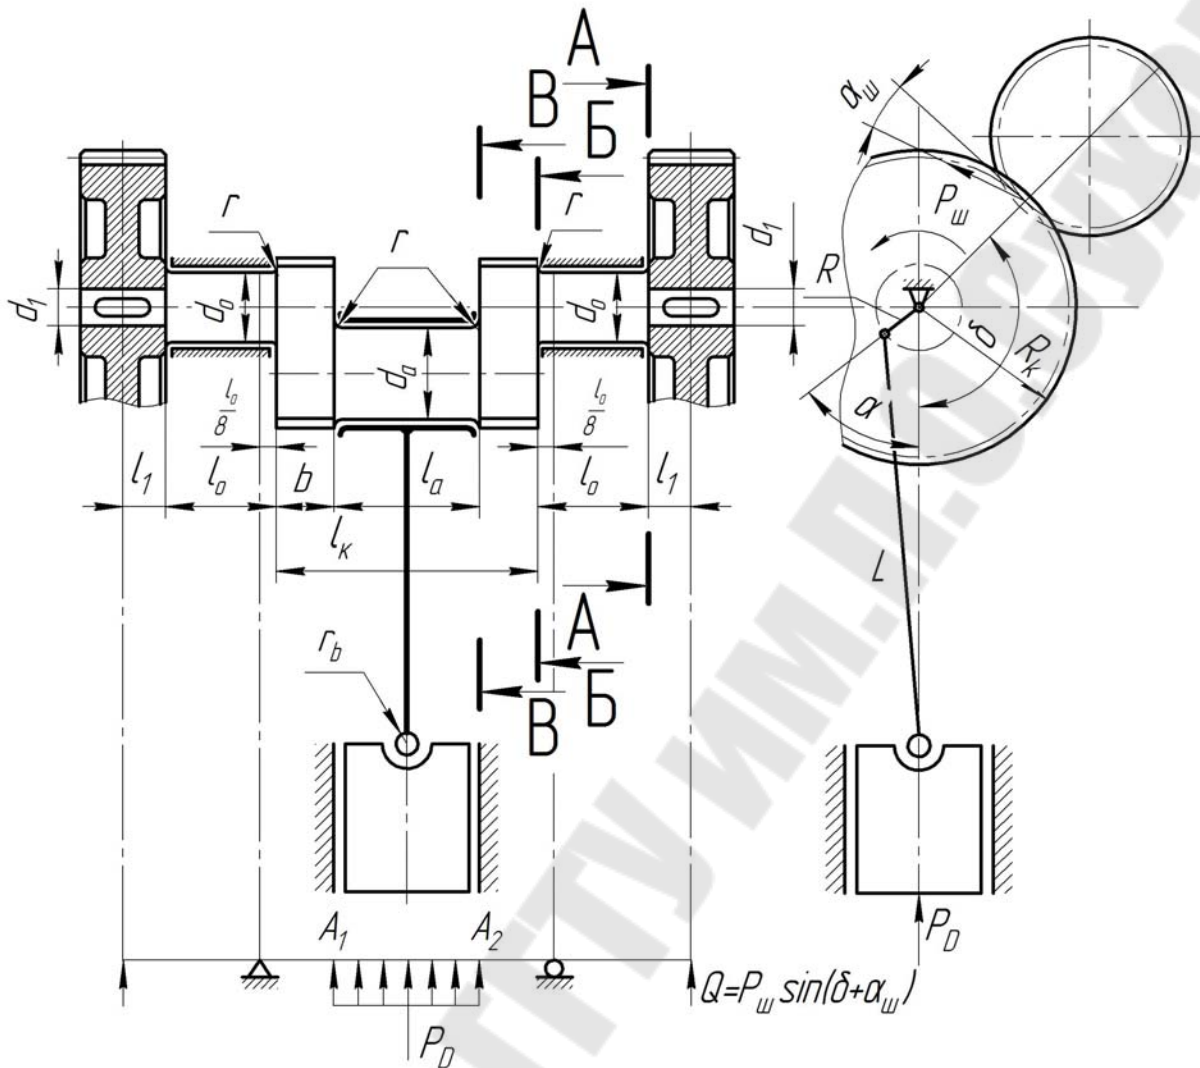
Одноколенчатый вал с двухсторонним зубчатым приводом
